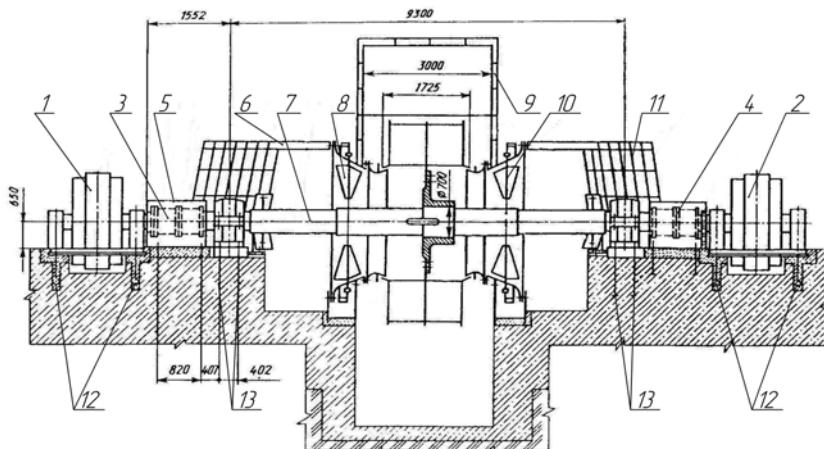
Вентилятор ВЦД-47,5 УМ с анкерными болтами подшипников электродвигателей и вентилятора: 1, 2 – электродвигатели; 3, 4 – зубчатые муфты; 5 – ограждение муфты; 6 – левое входное устройство (коробка); 7 – ротор; 8 – левый направляющий аппарат; 9 – корпус; 10 – правый направляющий аппарат; 11 – правое входное устройство (коробка); 12 – анкерные болты подшипников электродвигателей; 13 – анкерные болты подшипников вентилятора
